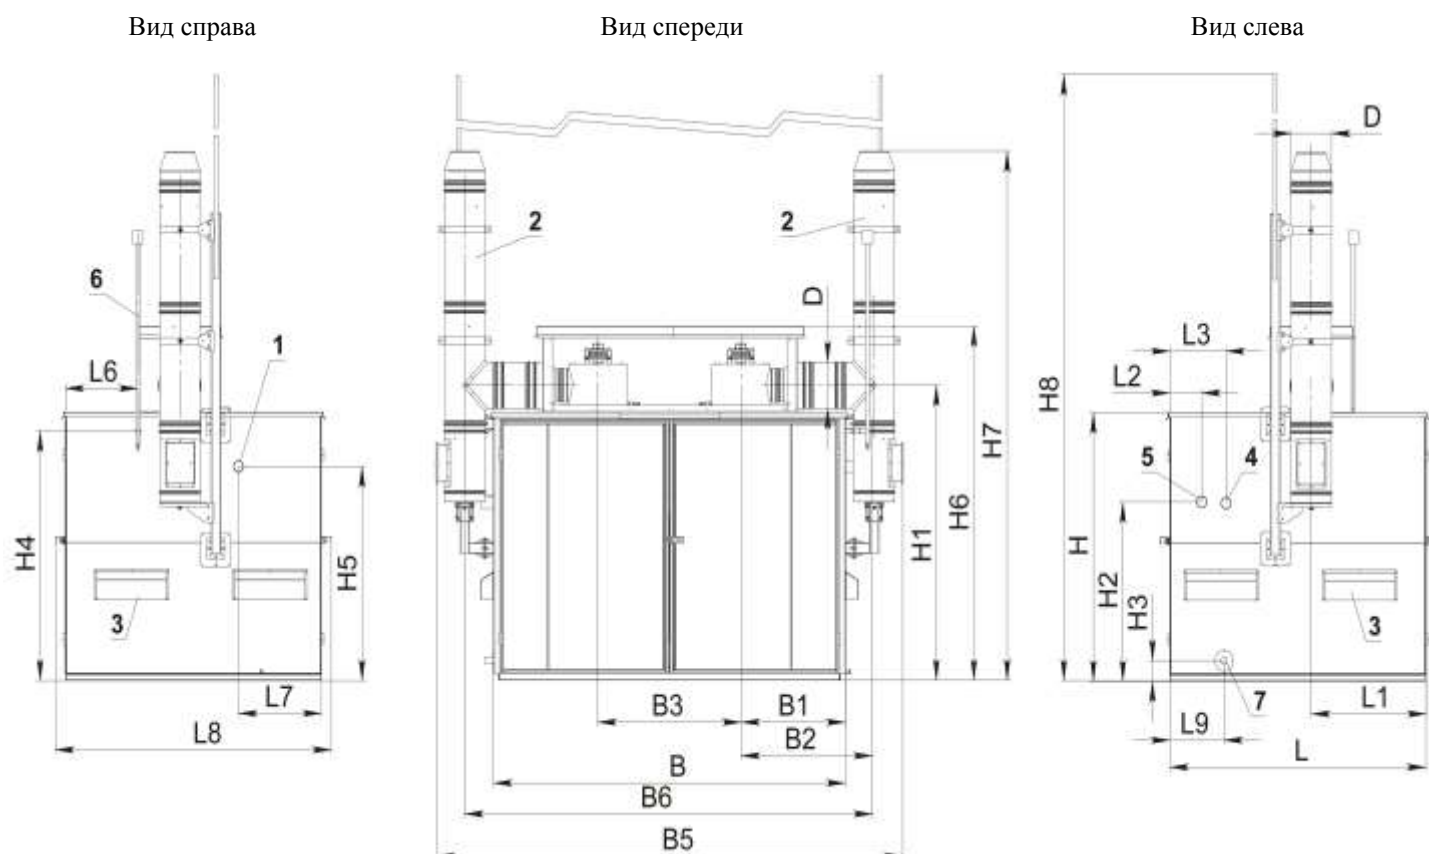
Габаритно-присоединительные размеры с дымоходами для котлов RSH400, RSH500, RSH600, RSH800.
